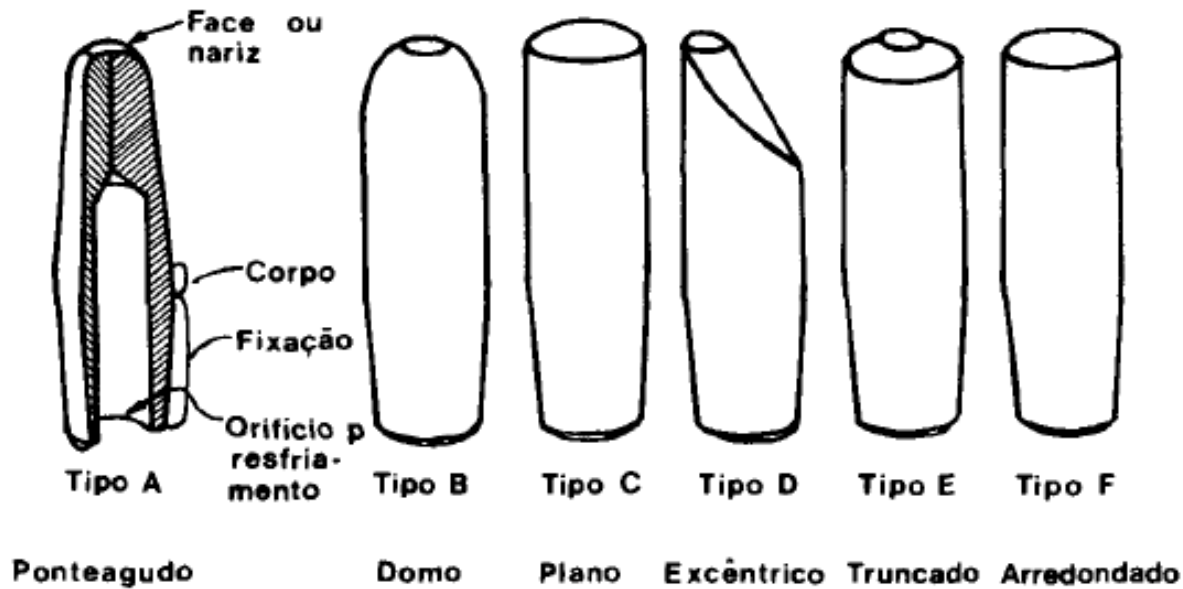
Tipos padrões de eletrodos para a soldagem por ponto
